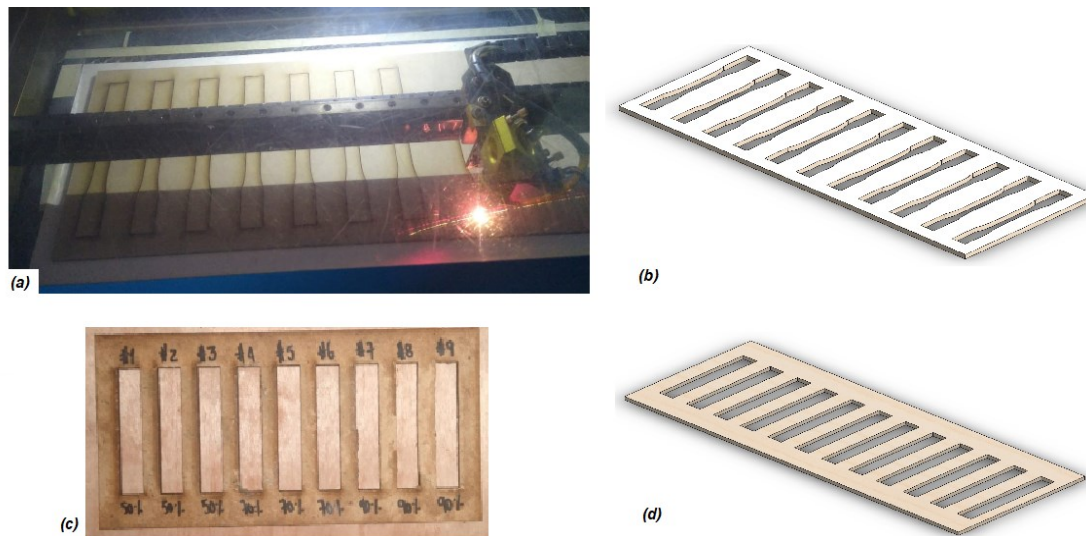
(a) Corte Láser, (b) Molde de tracción, (c) Molde de Impacto, (d) Molde de flexión. Elaboración propia
